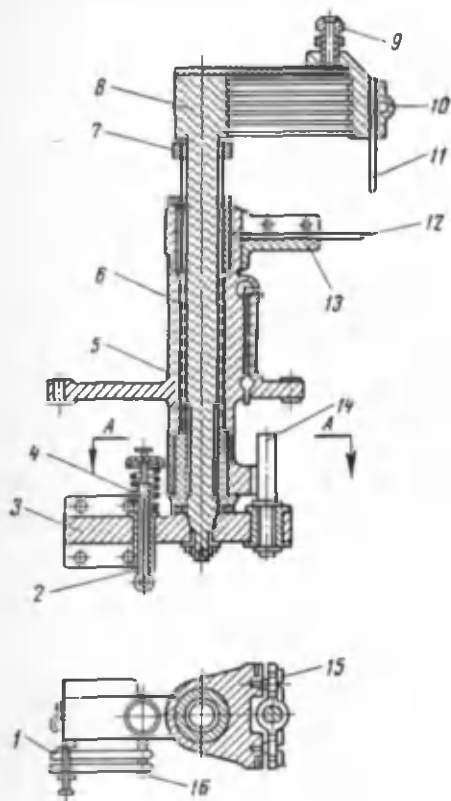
Сварочный клюв монтажно-сварочного стола:
